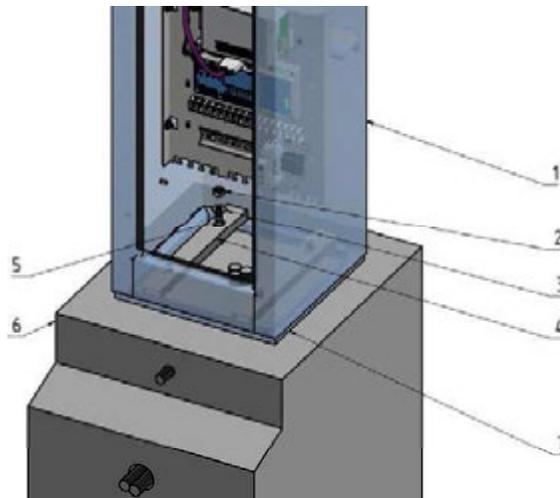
Monter le boîtier (ici avec le kit de montage PROACCESS)
